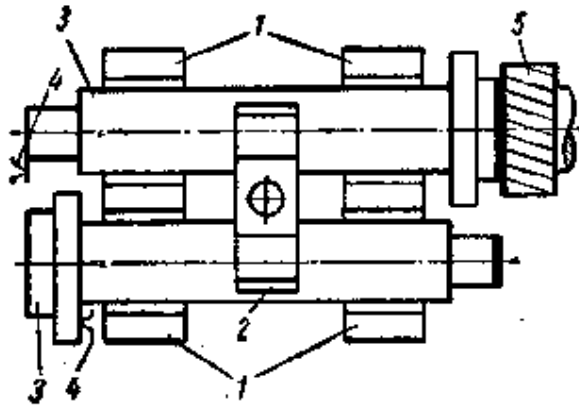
Схема фрезерування торців двох заготовок на горизонтально-фрезерувальному верстаті: 1 – установочні призми; 2 – затискаюча планка; 3 – оброблювані заготовки; 4 – упори; 5 – фреза
